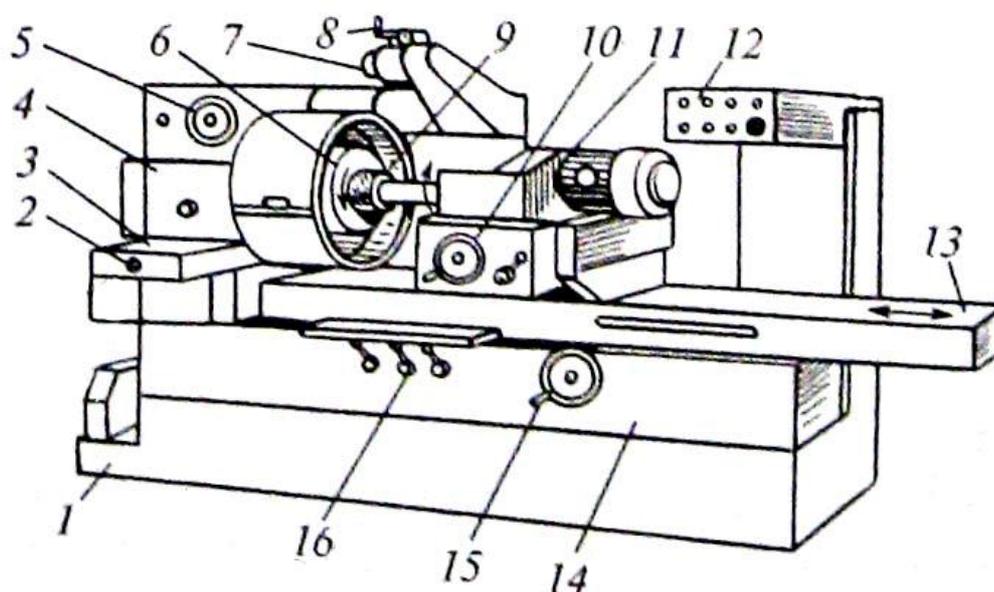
Станок внутришлифовальный; 1 – станина; 2 – механизм поперечной подачи изделия; 3 – подвижная плита; 4 – бабка изделия; 5 – маховик ручной подачи изделия; 6 – изделие; 7 – абразивный круг для торцевого шлифования; 8 – рукоятка перемещения круга торцевого шлифования; 9 – круг для обработки внутренней поверхности изделия; 10 – рукоятка поперечного перемещения шлифовального суппорта; 11 – суппорт шлифовального круга; 12 – пульт управления станком; 13 – стол; 14 – кожух стола; 15 – рукоятка продольного перемещения стола; 16 – упоры продольного перемещения
